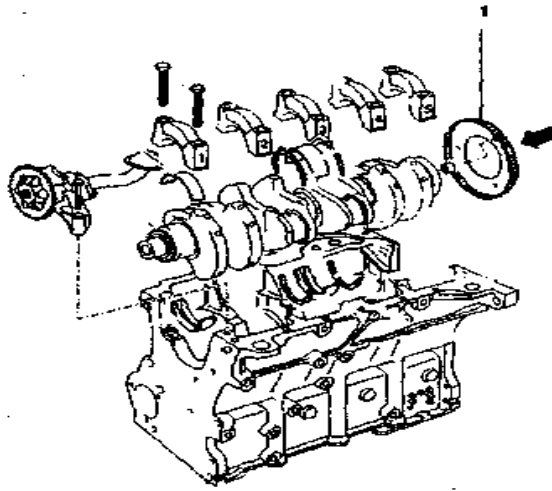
Розташування імпульсного колеса на двигуні
